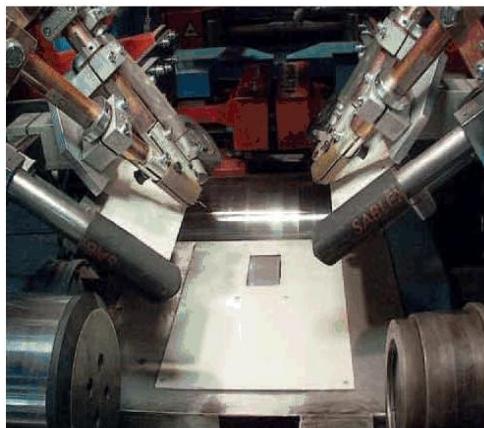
Расположение сварочных головок постоянного и переменного тока в машине для сварки балок таврового профиля
